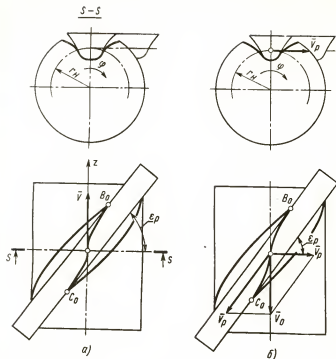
Схема сопряжения винтовой поверхности детали с инструментальной рейкой
